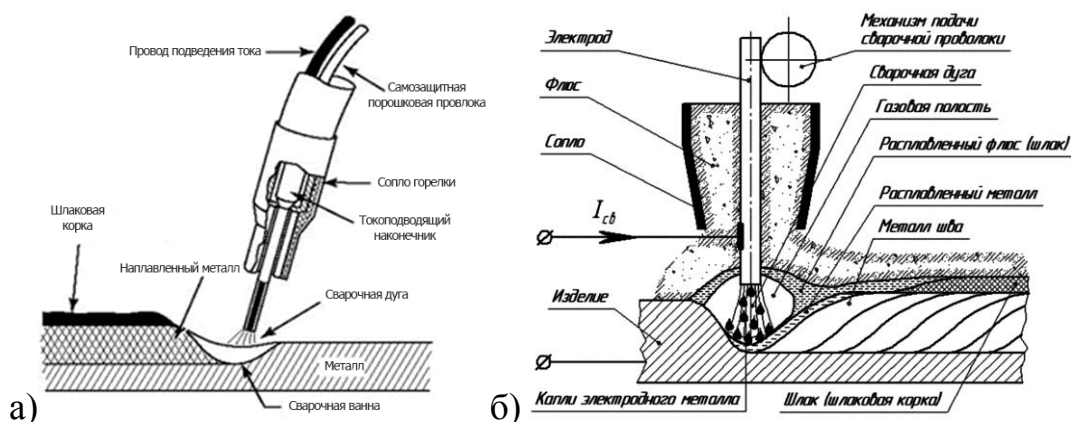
Альтернативные способы сварки: порошковой самозащитной проволокой (а) и автоматической сварки под флюсом (б)
